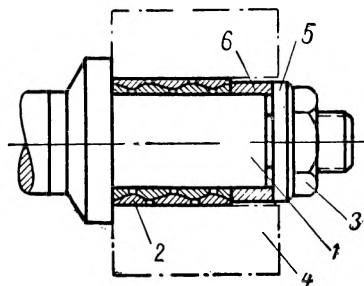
Оправка с кольцевыми пружинящими уплотнителями для зажима заготовки за внутреннюю поверхность.
